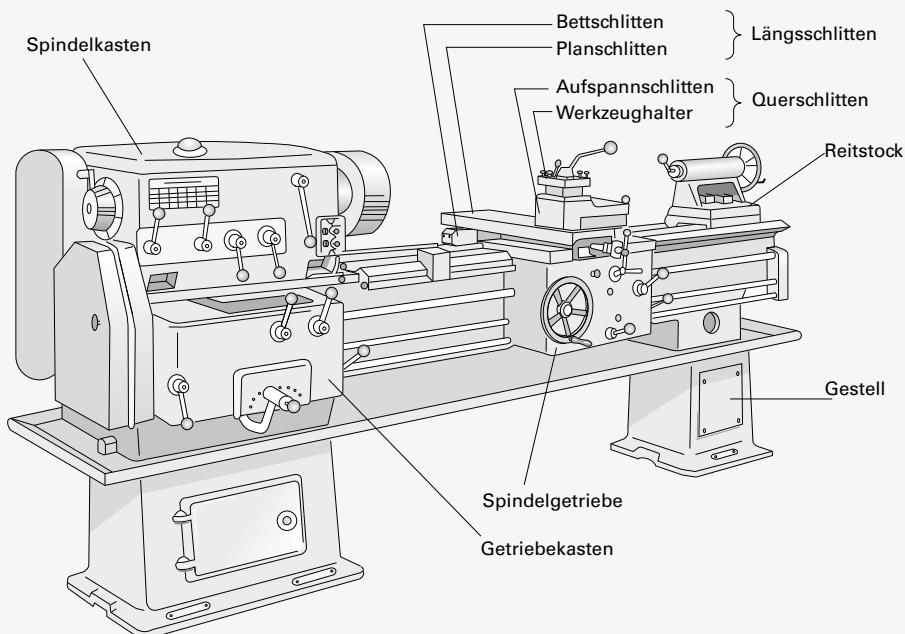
Drehmaschine, aus mehreren Baugruppen zusammengesetzt
